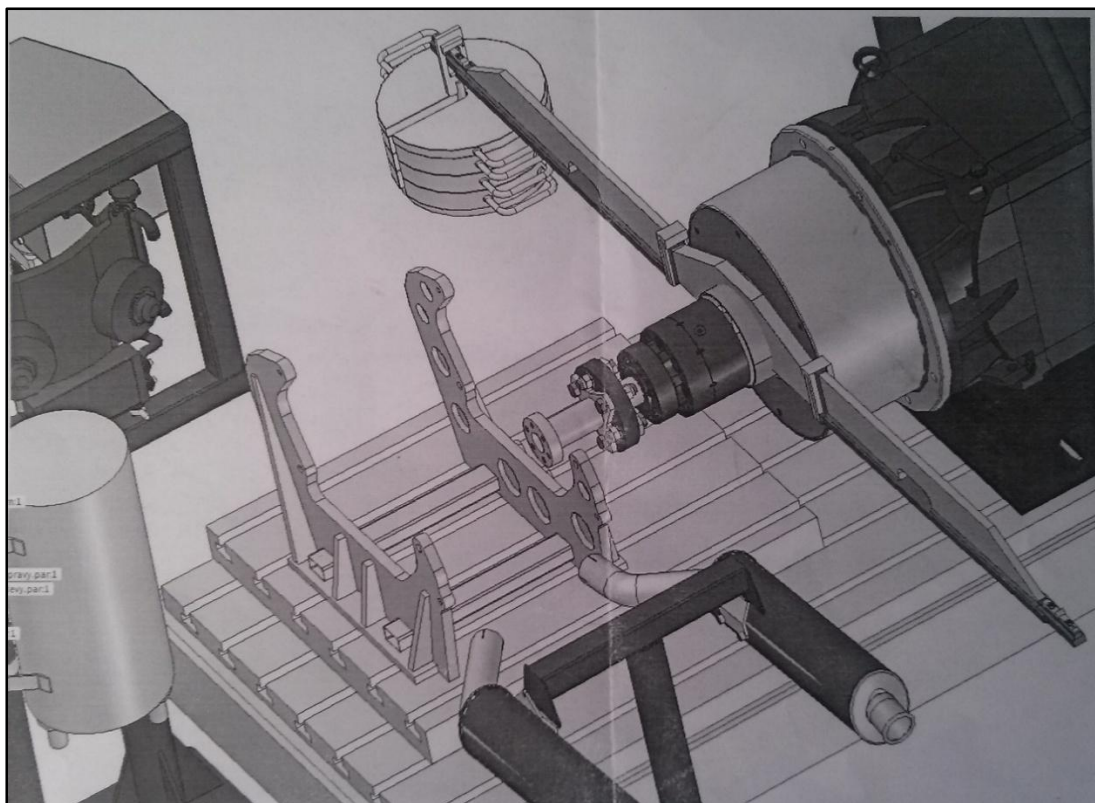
Odpružená deska: 1 – plynové pružiny; 2 – dynamometr; 3 – podstavné nohy; 4 – rám motoru; 5 – spojovací hřídel;
